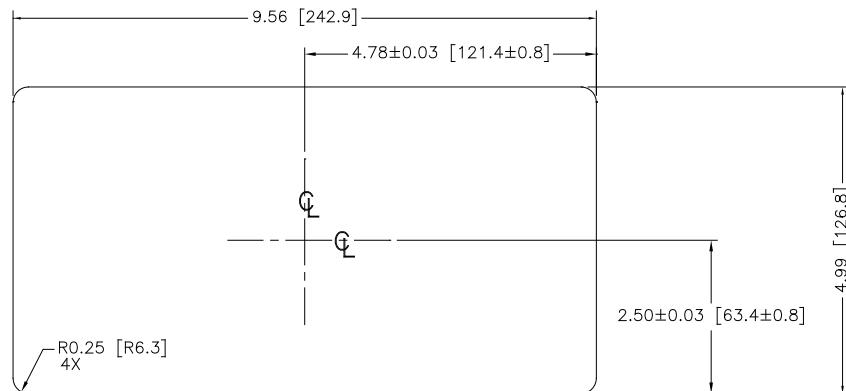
Dimensiones del recorte para montaje en panel del IND560
